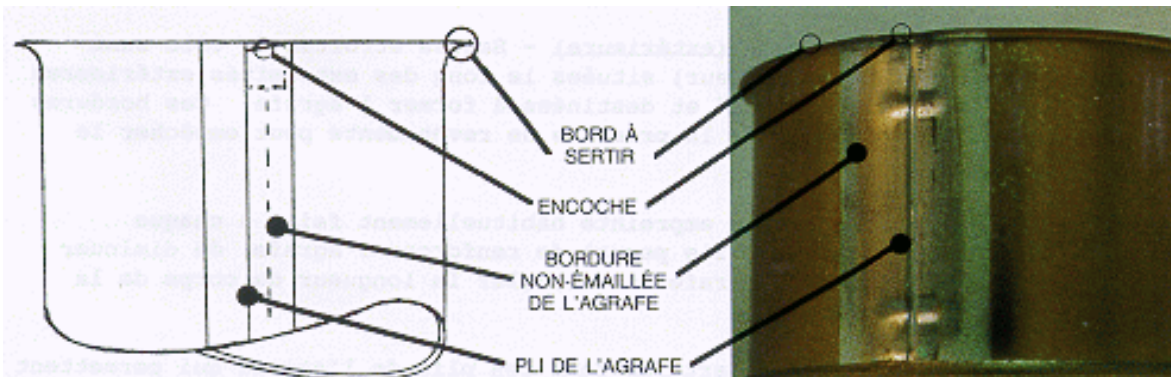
b - Boîte trois pièces - Agrafe soudée à l'étain - Boîte ouverte
